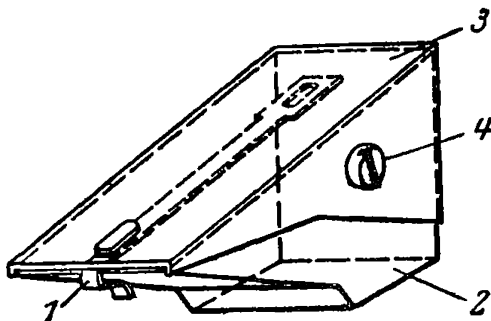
Приспособление для обработки рабочих поверхностей контактов.
